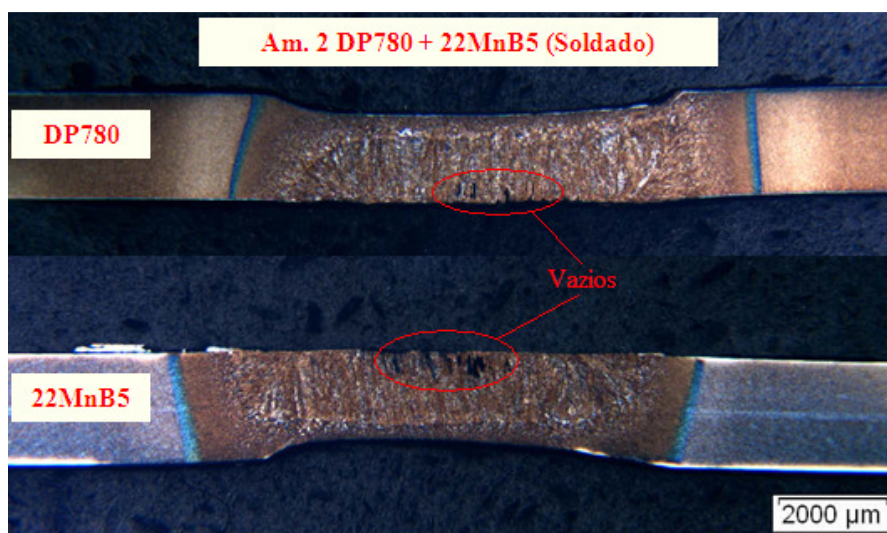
União soldada DP780 – TL4255 (20X).
